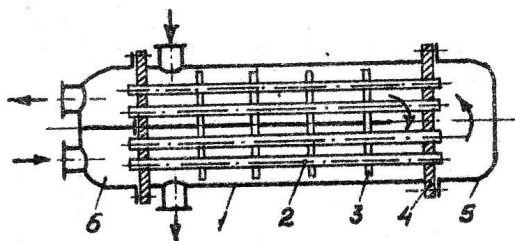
Кожухотрубчатый теплообменник жесткого типа: 1 - корпус; 2 - трубный пучок; 3 - перегородка; 4 - трубная решетка; 5-6 - крышки
